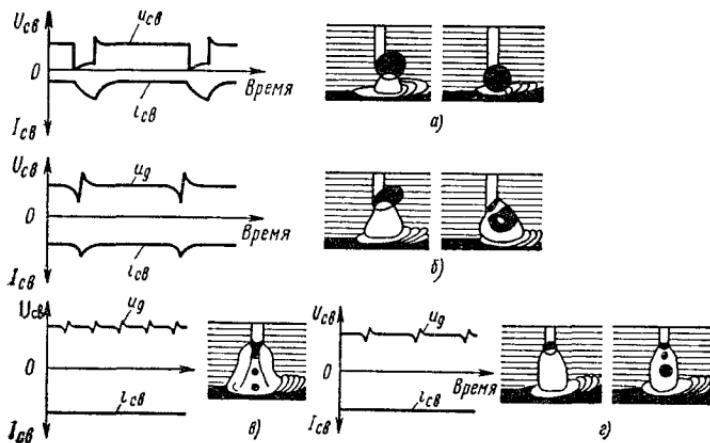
Внешний вид разрядного промежутка и осциллограммы напряжения и тока сварки (i_{cb} — сила тока)
